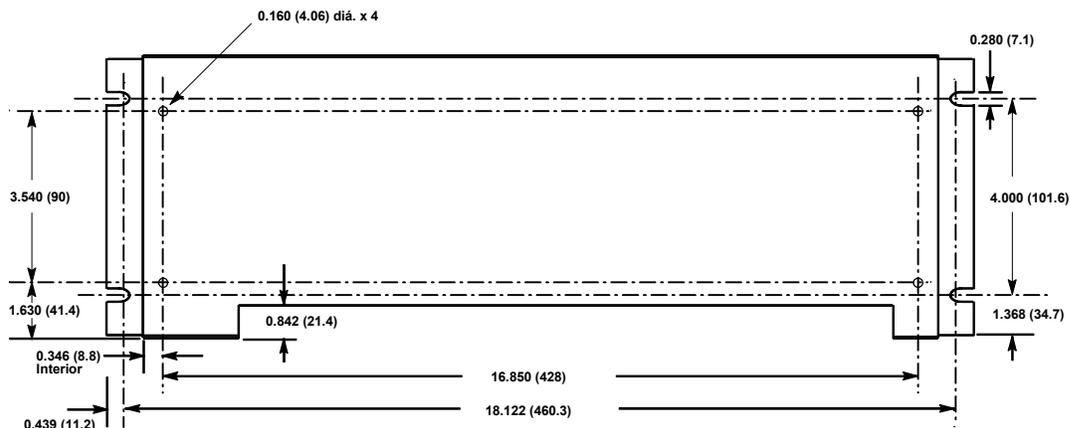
Instalación del soporte adaptador para montaje frontal IC693ACC308
